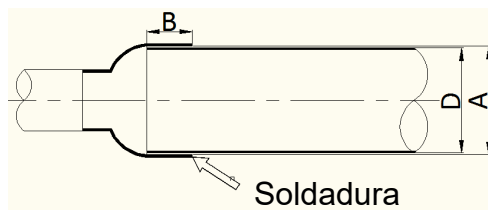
Orientación de tuberías durante la soldadura
